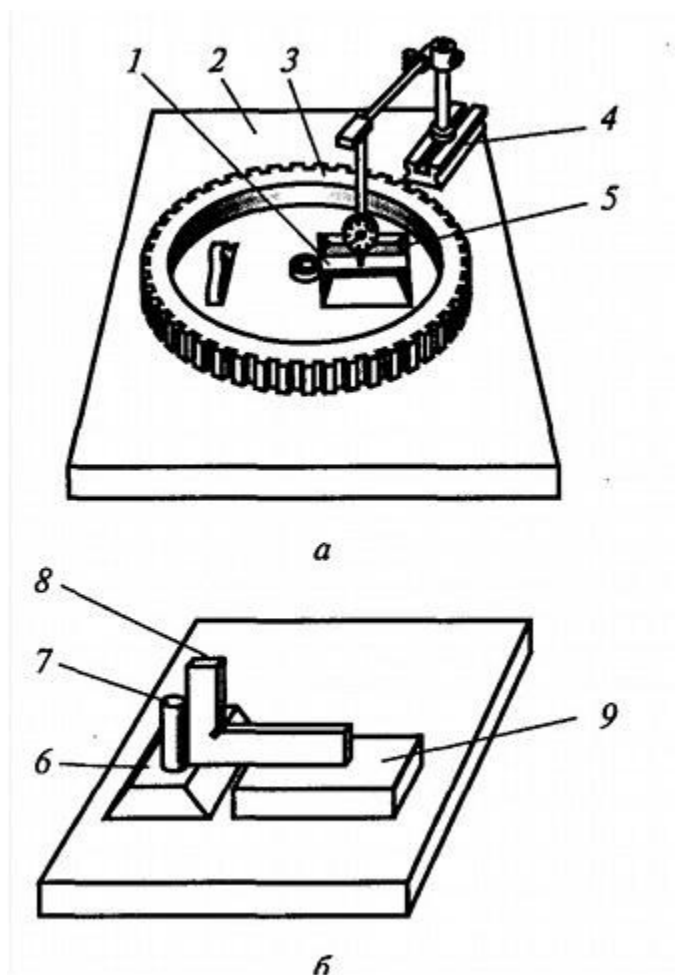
Приспособления для контроля ремонта кулисного зубчатого колеса (а) и ползушки (б): 1 и 5 — направляющие поверхности; 2 — поверочная плита; 3 — зубчатое колесо; 4 — стойка; 6 — ползушка; 7 — ось; 8 — угольник; 9 — плоскопараллельная плитка
